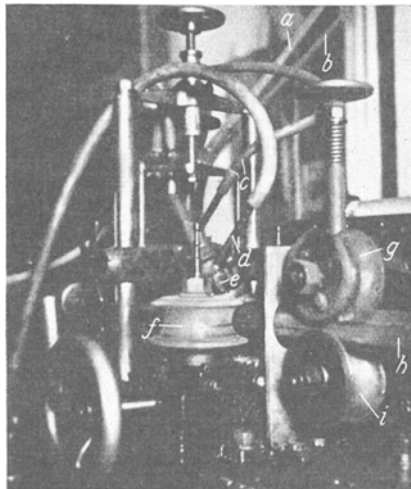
Teilansicht einer Rohrschweißmaschine.
